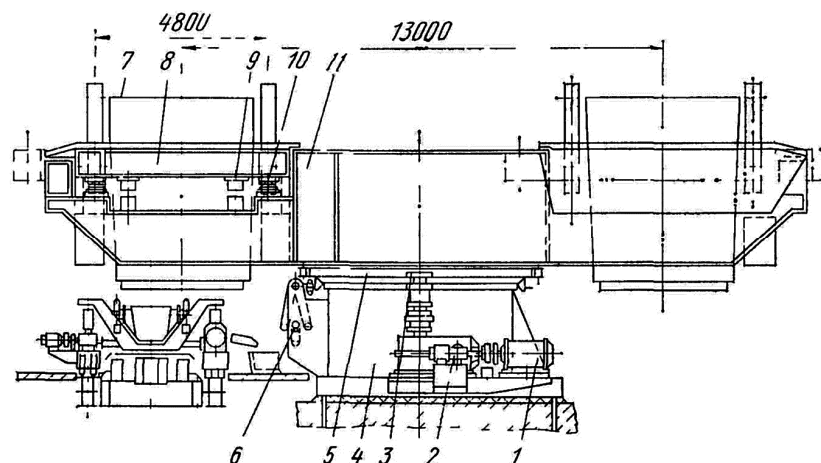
Поворотний сталерозливний стенд конструкції «Демаг»
